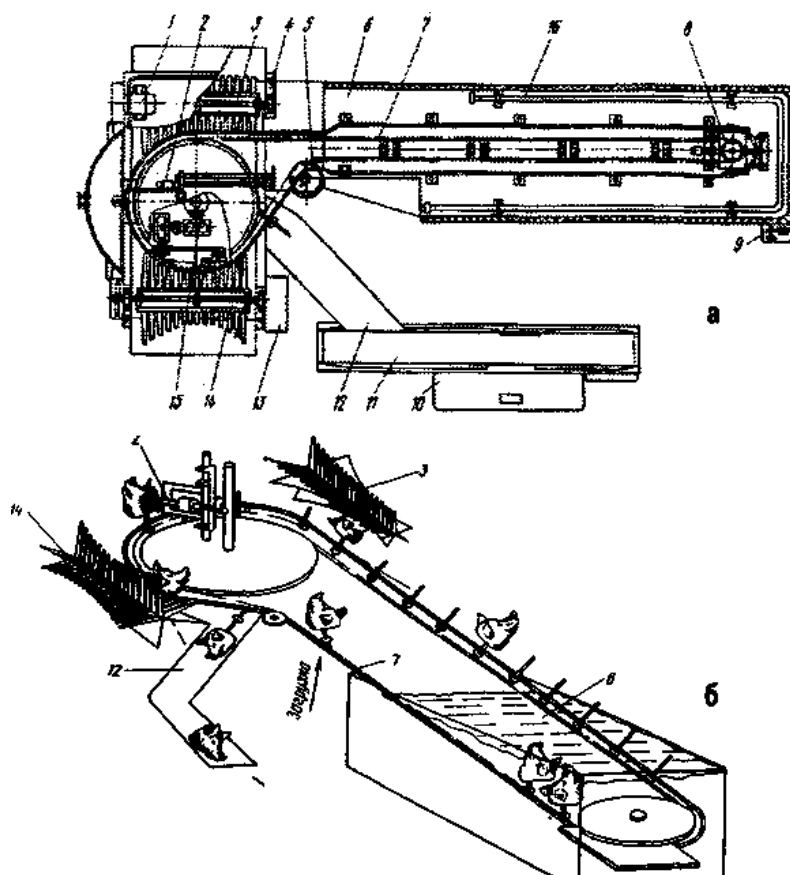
Технологічна схема агрегату для обробки свинячих голів ФГБ: 1 – привід бил, 2 – пристосування для обсмалювання, 3 – вал з билами для зняття щетини, 4 – вузол регулювання бил, 5 – механізм ручного привода, 6 – ошпарювальний чан, 7 – ланцюговий конвейер, 8 – натяжна станція, 9 – заслінка для зливання води, 10 – стіл для виймання мозку і гіпофіза, 11 – транспортер стрічковий, 12 – спуск для голів, 13 – пульт для перерозподілу повітря та гасу, 14 – вал з билами для зняття нагару, 15 – привод ланцюгового конвейєра, 16 – барботер для підігріву води.
